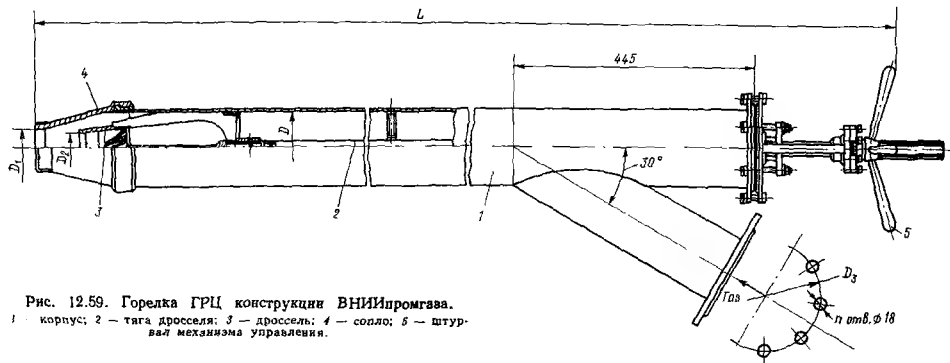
Горелка ГРЦ конструкции ВНИИпромгаза.
